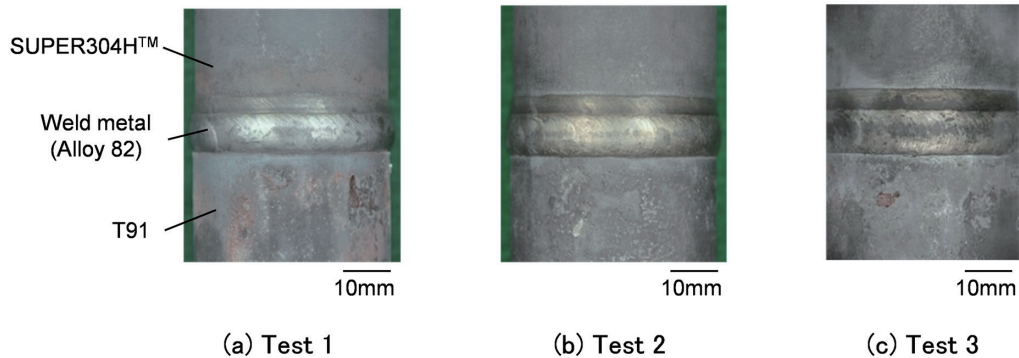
熱サイクル試験後の異材溶接鋼管の溶接部外観
